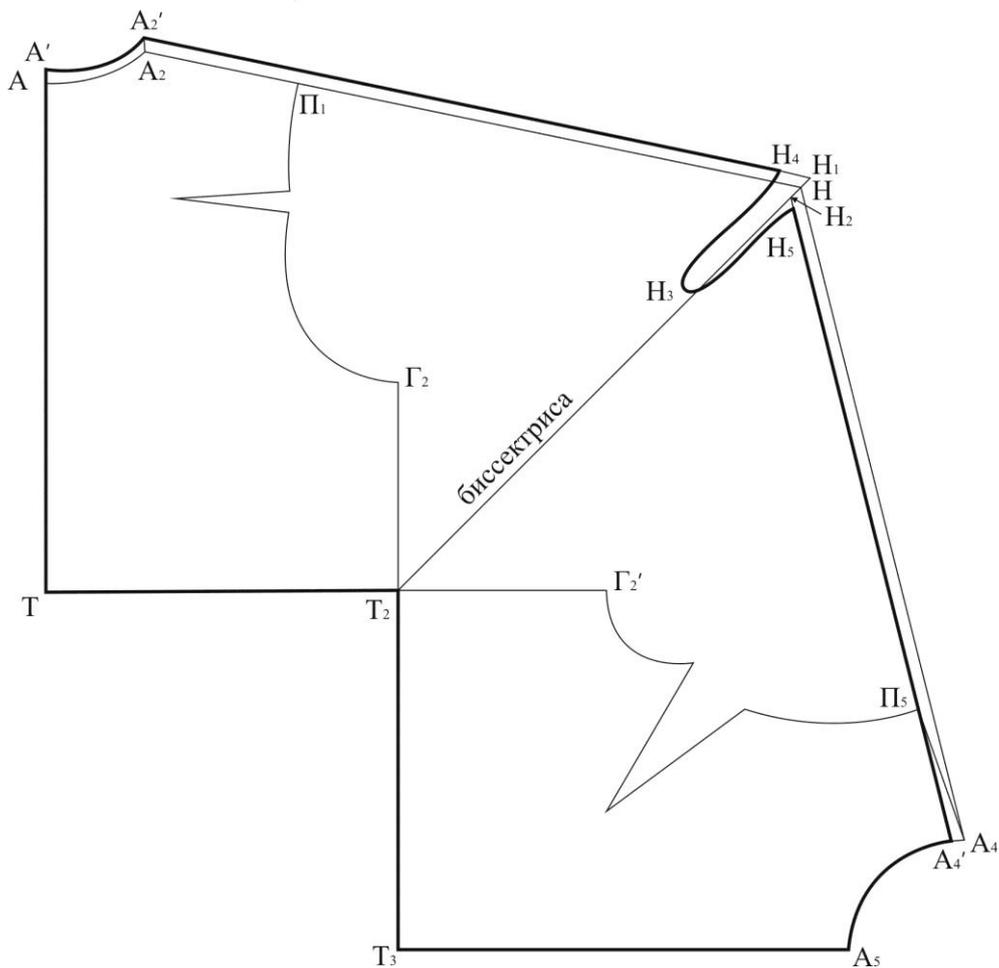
Пример оформления конструкции с цельнокроеным рукавом без бокового шва
